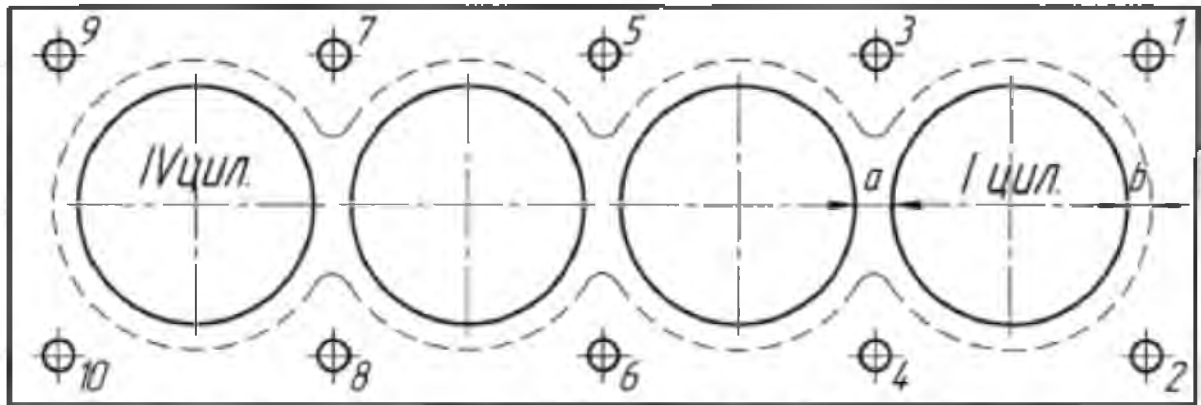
Схема групового різьбового з'єднання «головка блоку - блок циліндрів» рядного чотирициліндрового двигуна; 1-10 різьбових отворів у блоці циліндрів; а – товщина перемички між циліндрами; b - товщина стінки циліндра
